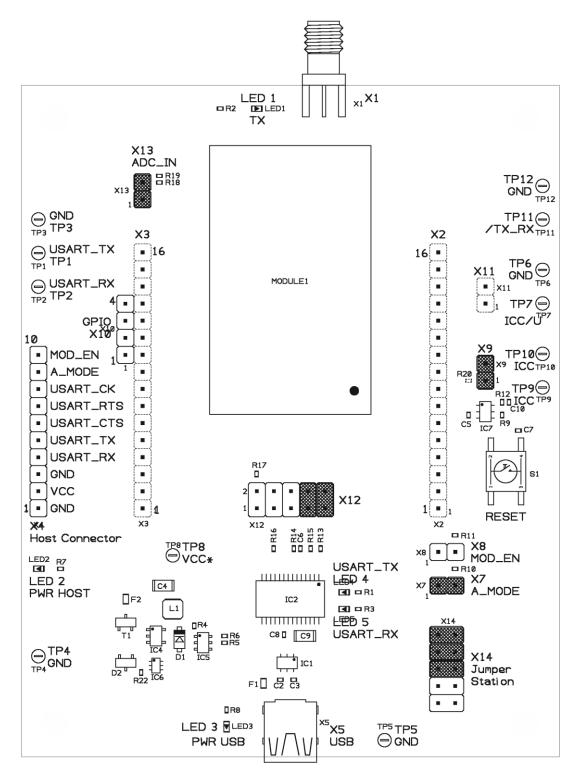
Swarm bee LE DK+ Board, assembly and connector configuration
